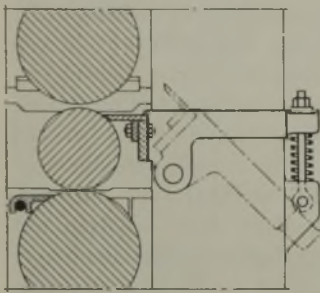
Walzarmatur zur Mittelwalze eines Dreiwalzen-Blechgerüsts.
